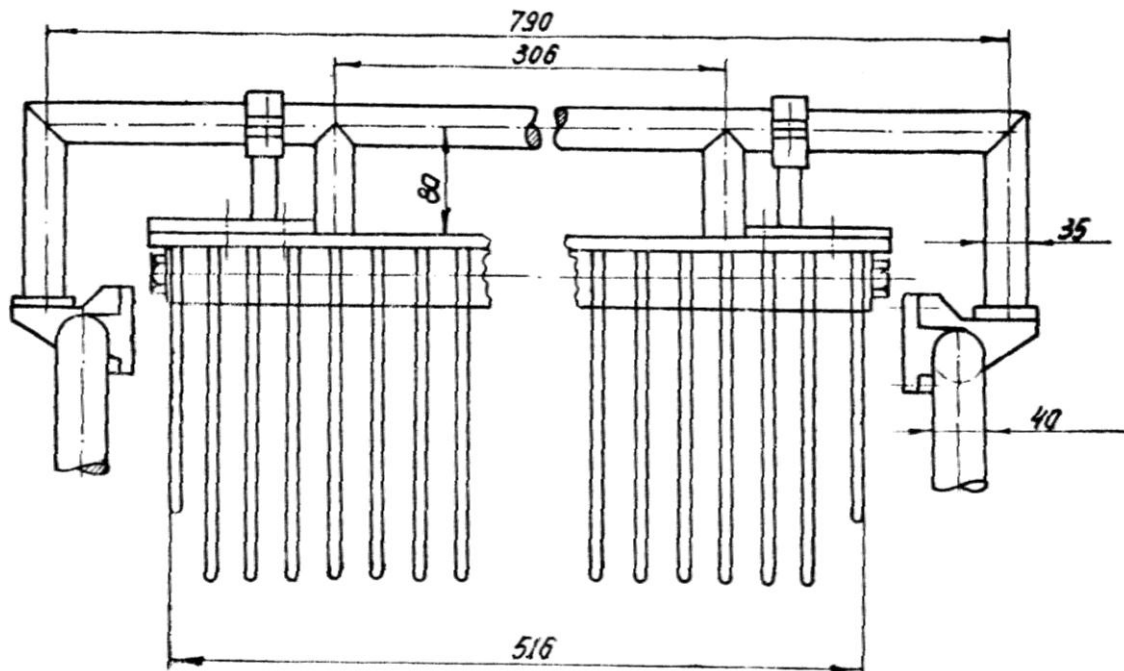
Конструкция крепления индуктивных пакетов вариатора
